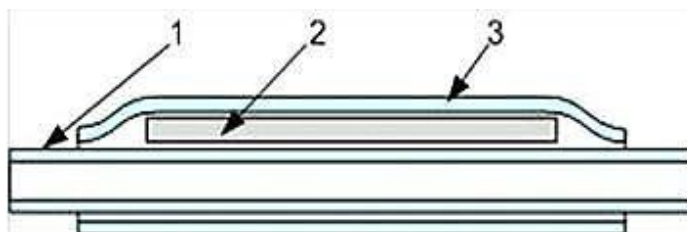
Комплект деталей для захисту місця зварювання [6.9].
